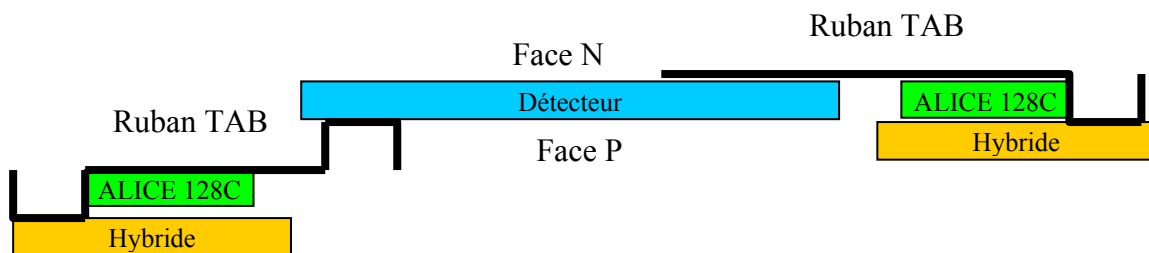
Cambrage des rubans TAB pour l'assemblage sur le module
